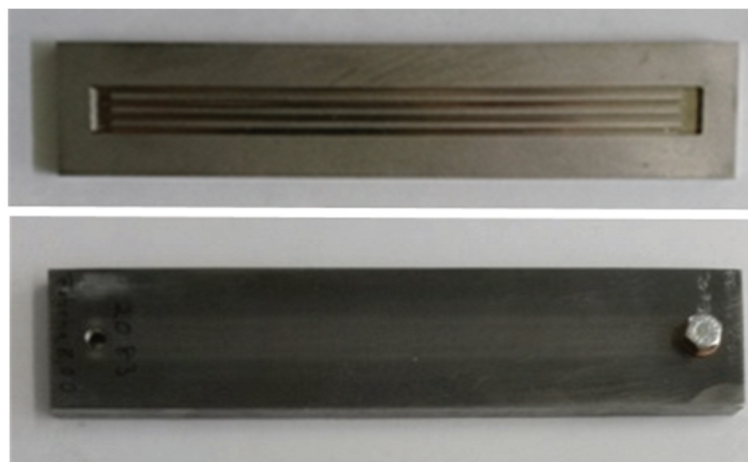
Aufnahmen der Schweißprobe aus Alloy800. Oben: Grundplatte vor dem Schweißen. Unten: Schweißprobe im Endzustand.
